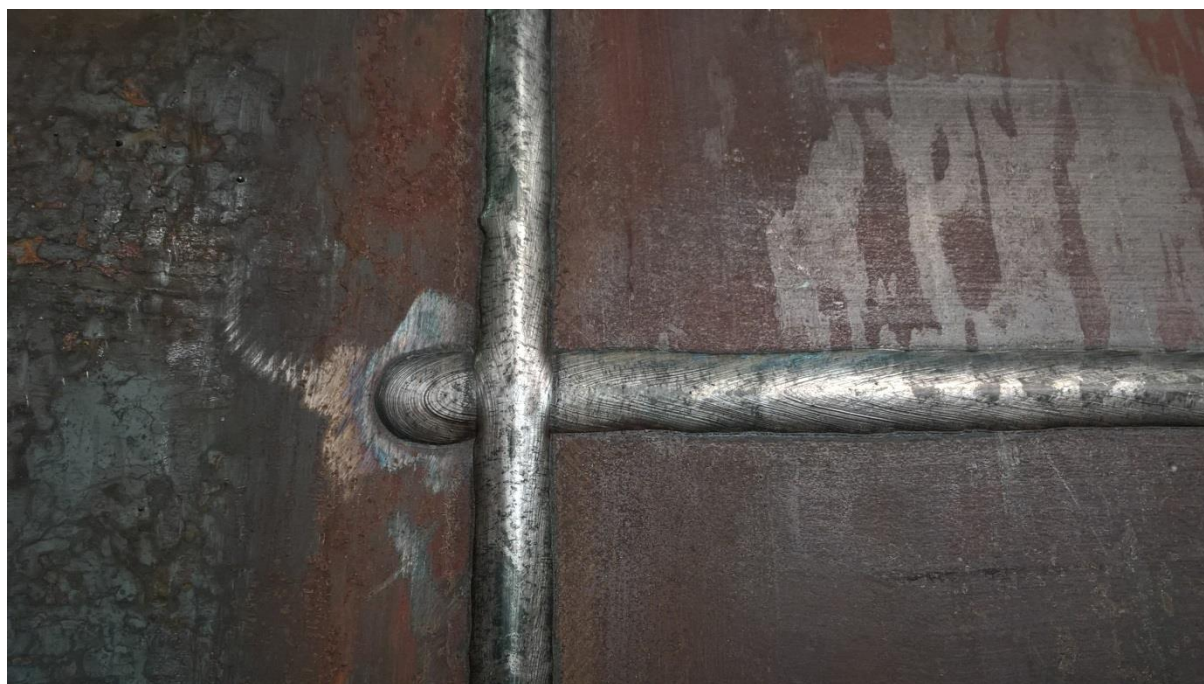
Фото сварного соединения С7 по ГОСТ 8713-79
